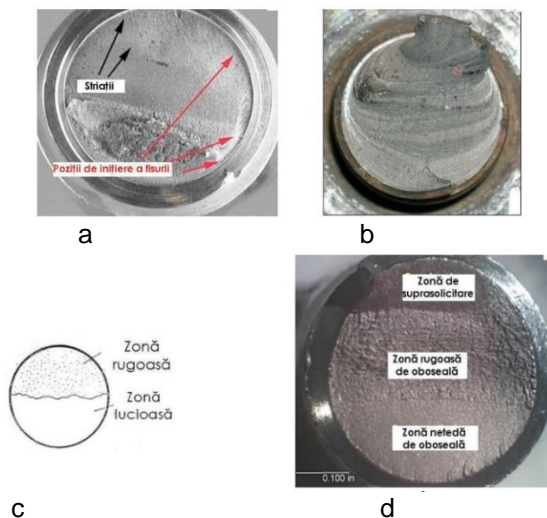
Aspectul secțiunii de rupere prin oboseală
